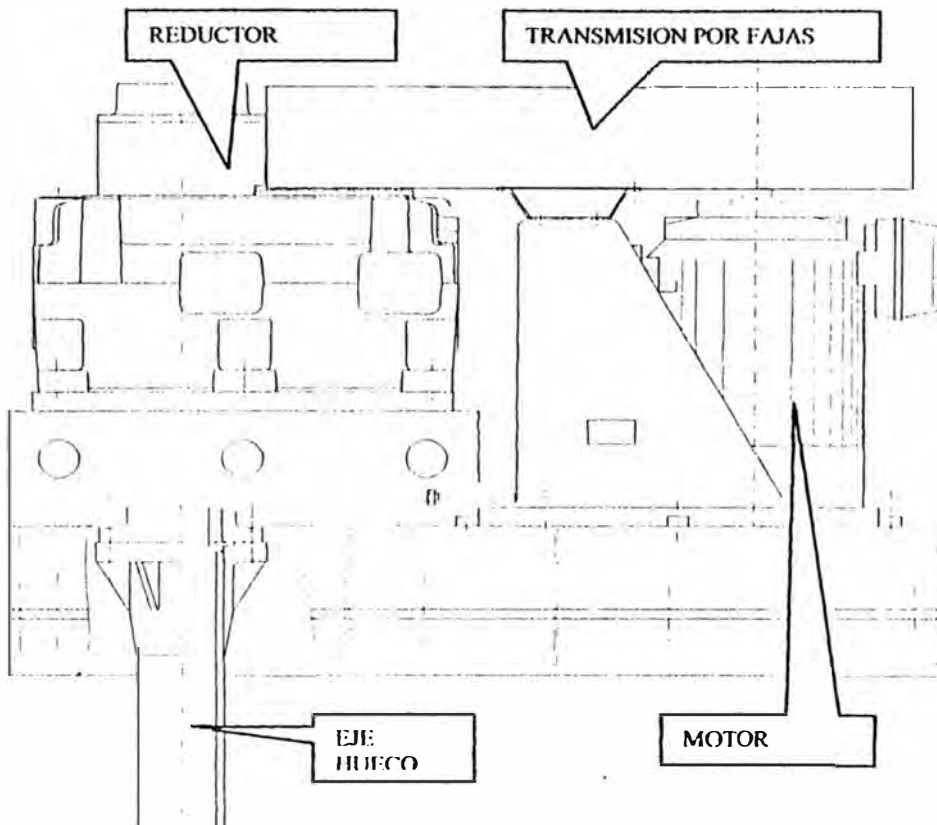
Vista lateral de un impulsor de reductor de velocidad con engranaje
